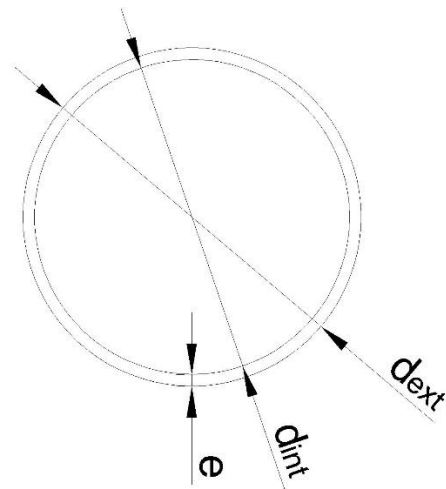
Dimensiones de perfil tubular. Fuente: Elaboración propia.
